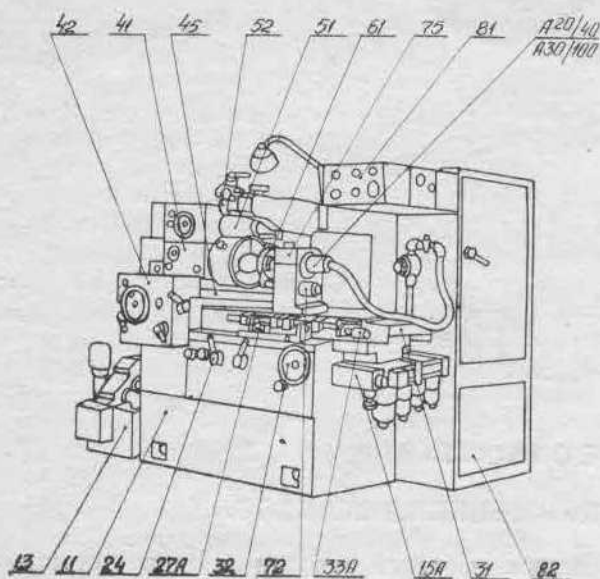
Общий вид станка мод. 3К225В с обозначением узлов.
